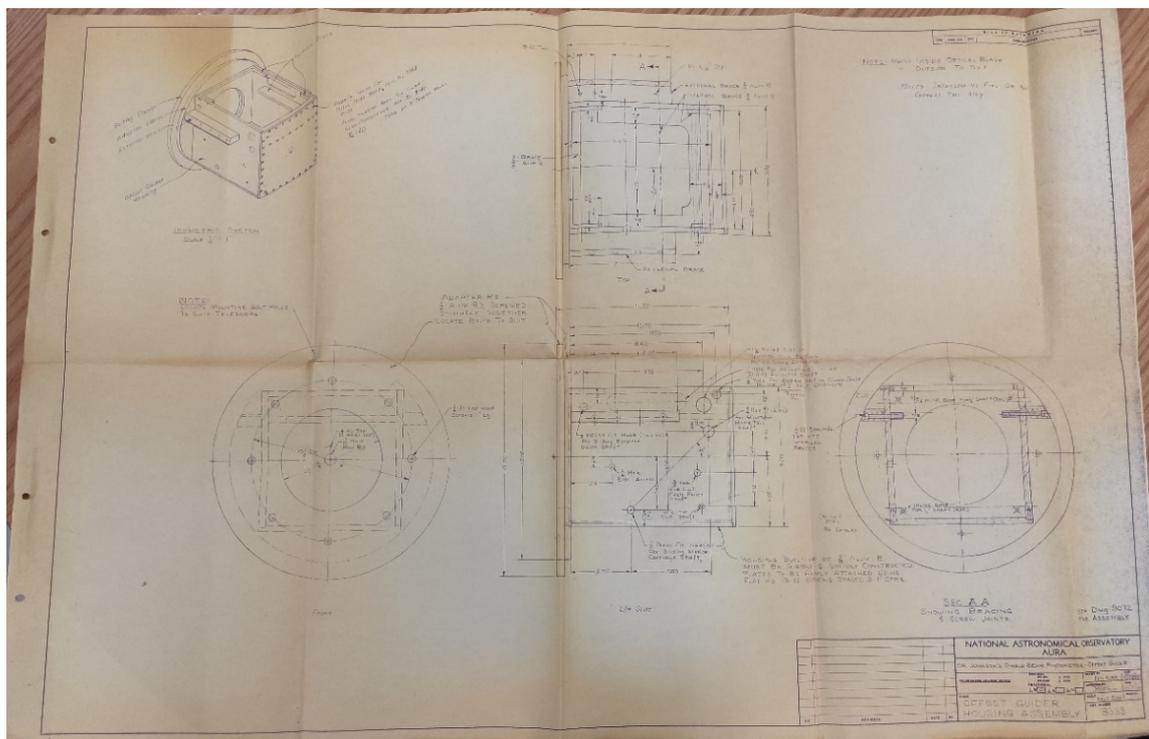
Copia del plano del ensamble del offset fotómetro para Tonantzintla. (Archivo Histórico del Instituto de Astronomía UNAM, Fondo Harold Johnson, caja 3)
